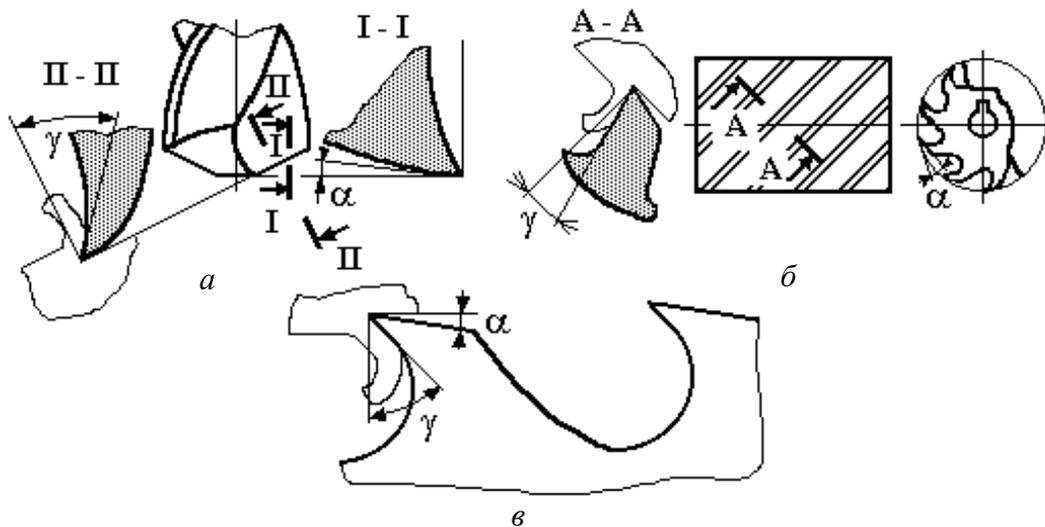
Передний и задний углы заточки зубьев многозубого лезвийного инструмента: *а* – спирального сверла; *б* – цилиндрической фрезы; *в* – круглой протяжки
